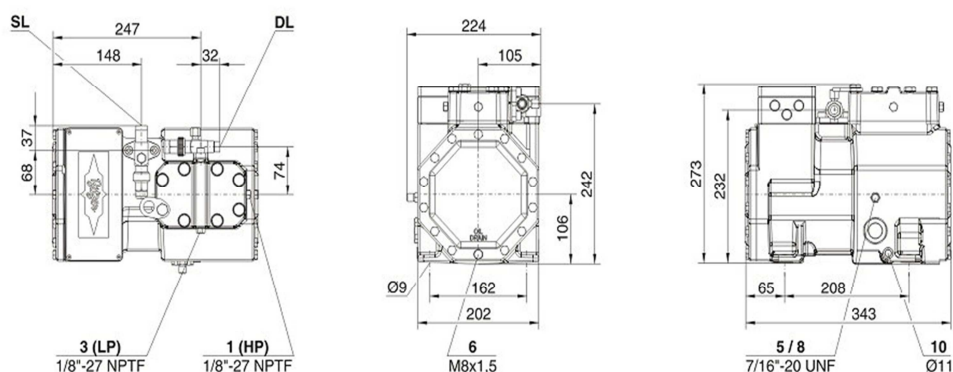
Dimensions del compressor 2KES-05Y 230/400V (40S).
